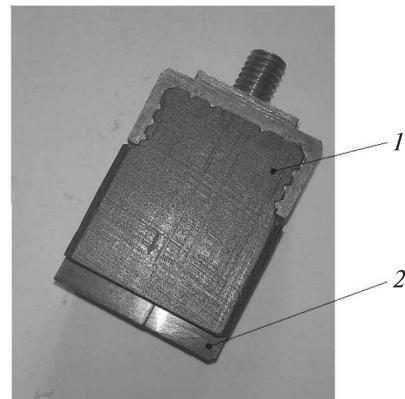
Вариант конструкции установки смазывающих щеток: 1 – смазывающая щетка; 2 – тело штатной электрощетки
